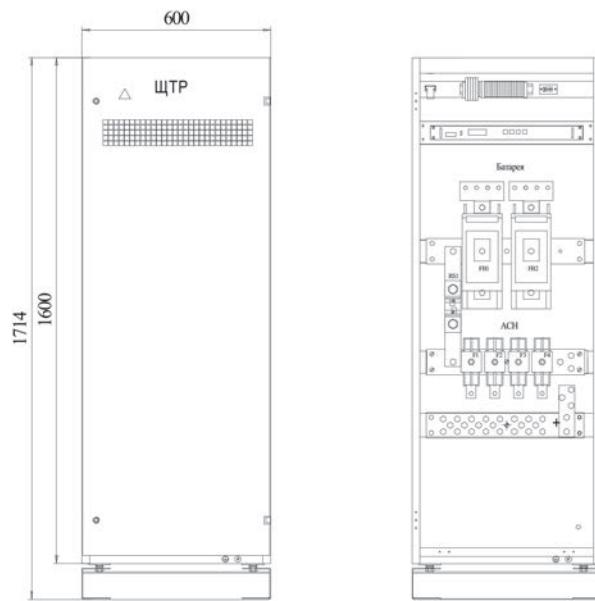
Габаритный чертеж ЩТР-4-В (глубина стойки 600мм)
